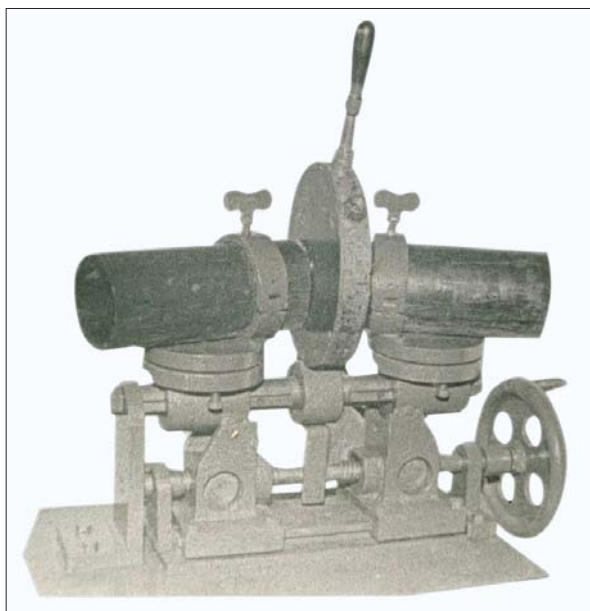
Экспериментальная установка с гидравлическим приводом для сварки труб встык
